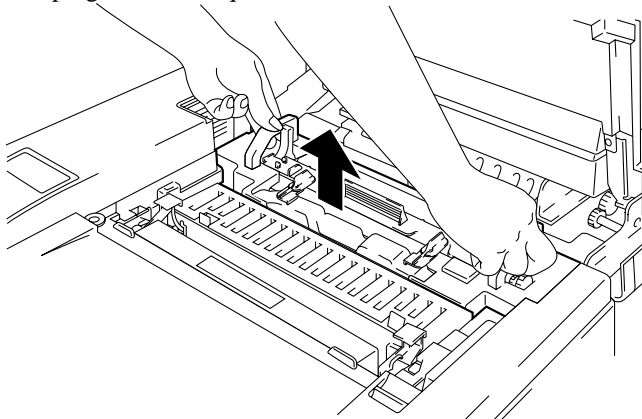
Extraction de l'ensemble de fixage de l'imprimante
